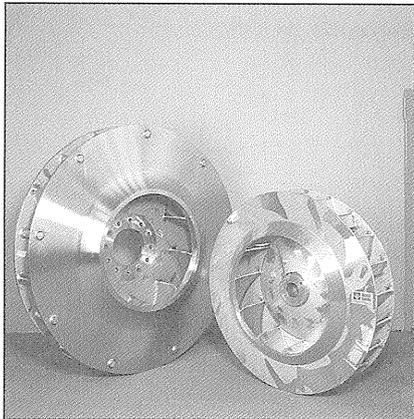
Ventilatorlaufrad wurde mit einem neuen Schutzgas geschweißt.
